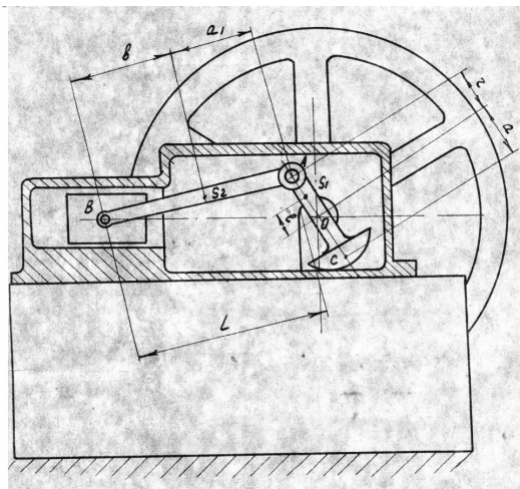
Схема компрессора с кривошипно-шатунным механизмом
